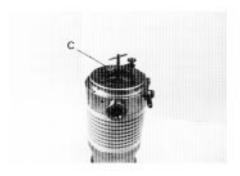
Werkzeug "C" befestigen Install tool "C" Fixer l'outil "C"
